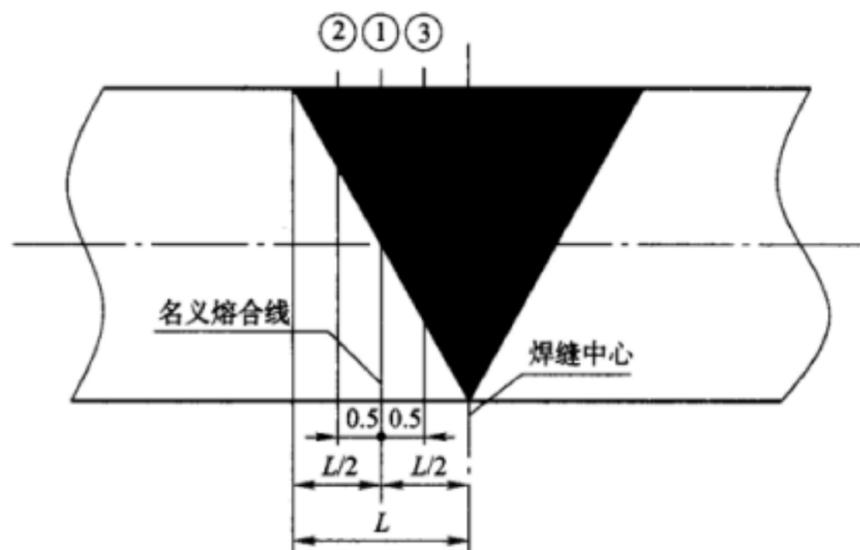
焊接接头冲击试验试样取样部位示意图
